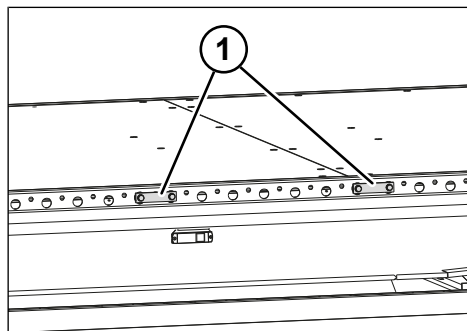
Opritorul fix Multi Belt la cadrul exterior Multi Lock
